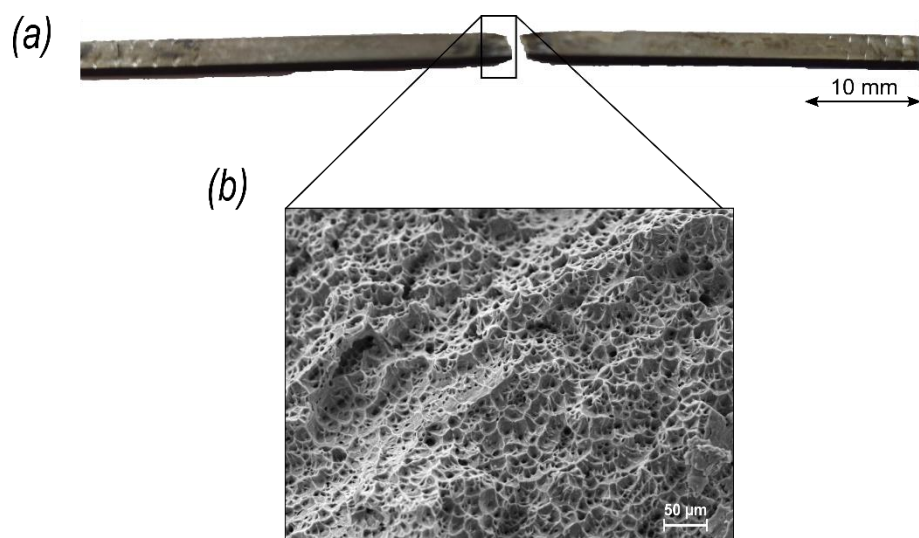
(a) #4_LAE_1_800°C_1H após ensaio de tração uniaxial. (b) Superfície de fratura.
